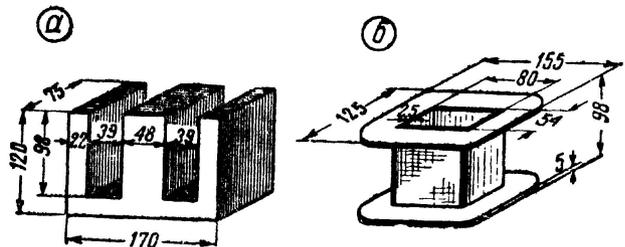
Детали дросселя размагничивающего устройства: а — сердечник; б — каркас для обмотки
